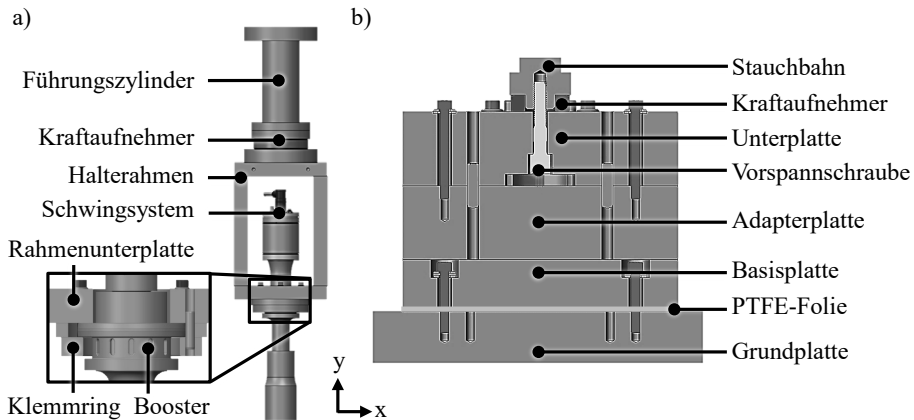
Konstruktive Werkzeuggestaltung: a) Oberwerkzeug und b) Unterwerkzeug
